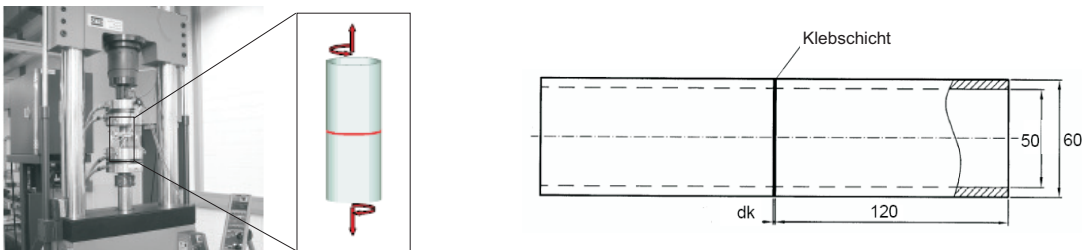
Prüfmaschine für Zug- und Torsionsbeanspruchung (links) der Rohrprobe (rechts) [3]
